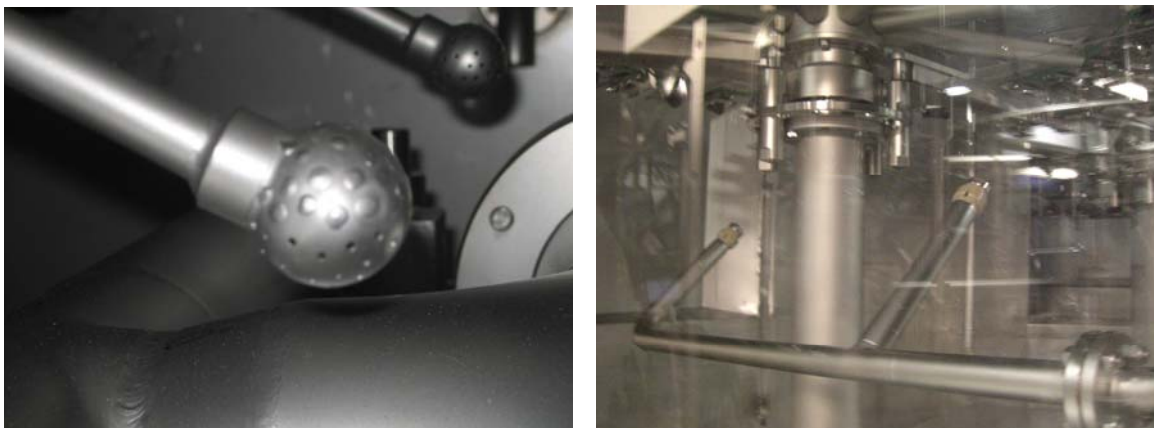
Spritzkugeln verschweißst (Mangel) / Düsen rotierend (QHD)
